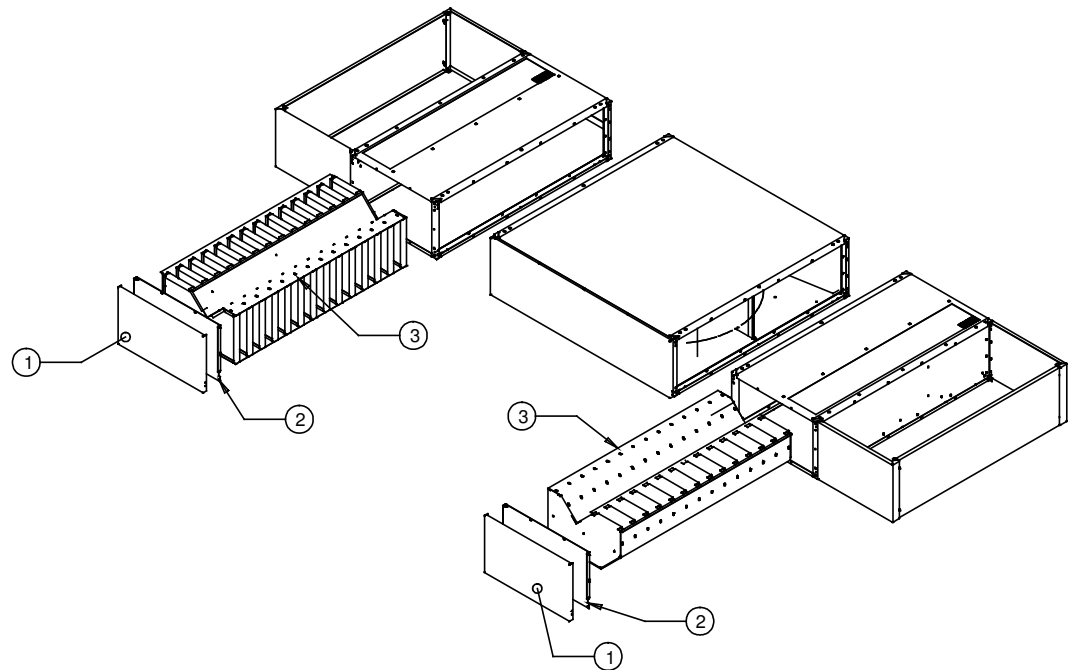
Einzelteile UB800 – UB1100 Schalldämpfer
